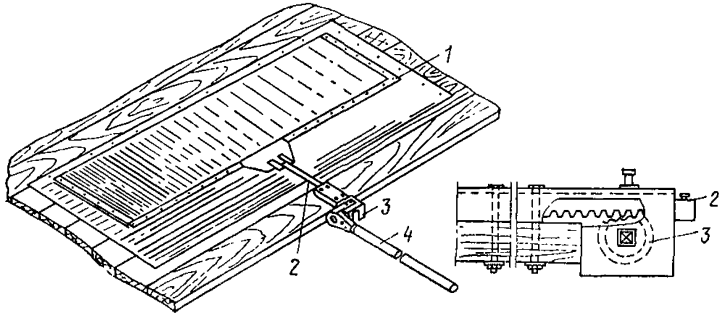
Приспособление для раздвижки пакетов силикатного кирпича
